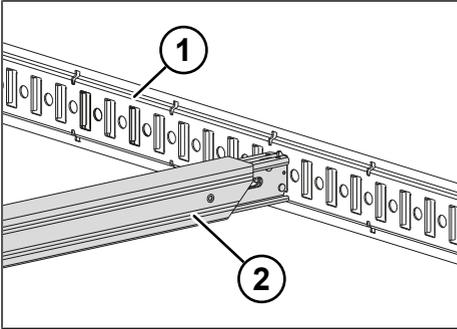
Guida di bloccaggio del carico con barre di bloccaggio
